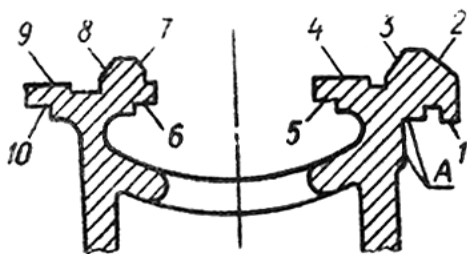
Переріз напрямних типової станини токарного верстата:
